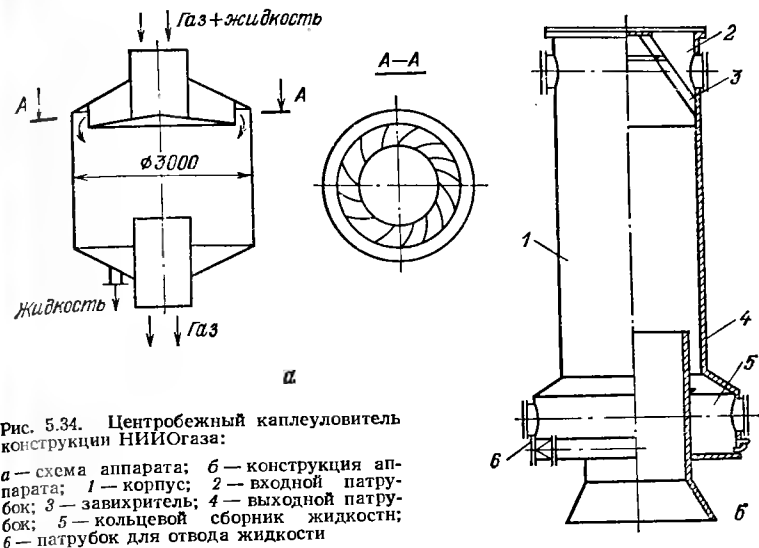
Центробежный каплеуловитель конструкции НИИОгаза:
